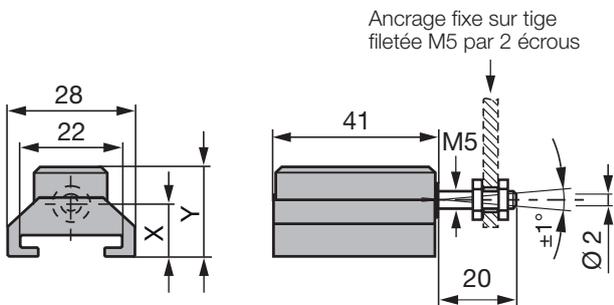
Dimensions de montage du capteur de position BTL5-M/N-2814-1S
